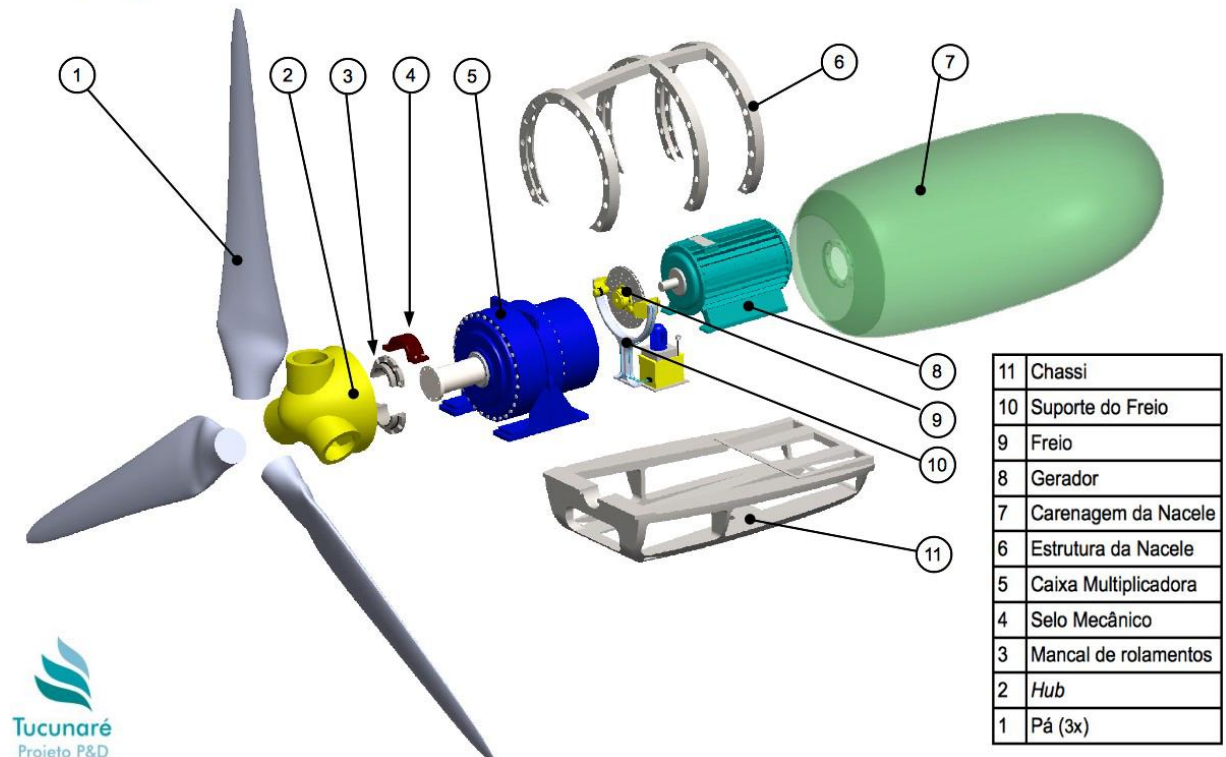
Vista explodida do conjunto de geração HTUC-01
